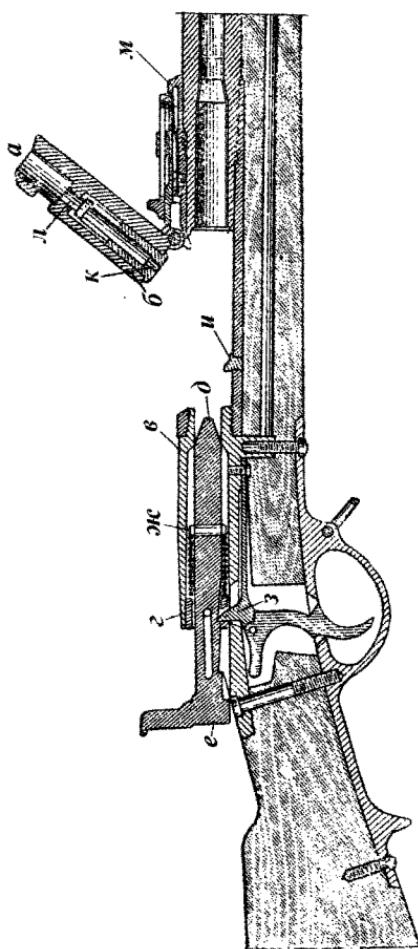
Устройство винтовки Бердан-1. Затвор открыт: аб — затвор; вг — замочная коробка; де — ударник с винтовкой боевой пружиной; ж — штифт упора боевой пружины; з — шептало; и — отражатель; кл — боек; м — спрелка.
